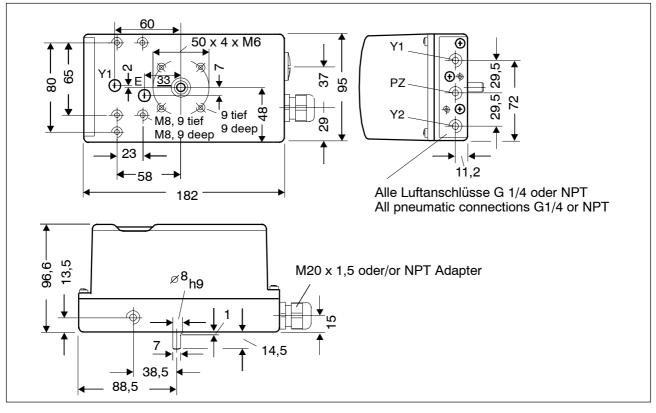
Maßbild Ausführung Kunststoffgehäuse
